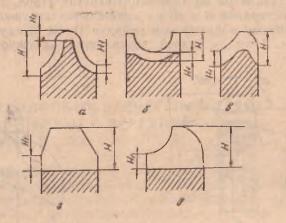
Согласование дна стружечной канавки с формой профиля зуба
